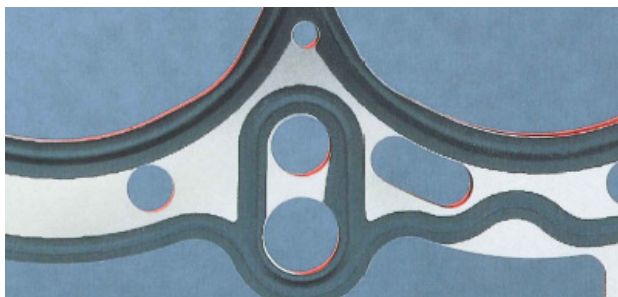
Zona de presión de aceite con reborde metálico debajo del vulcanizado negro.
